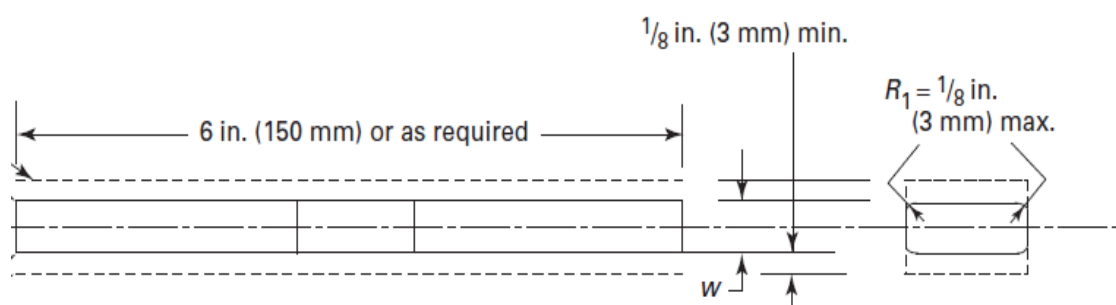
Croqui para usinagem corpo de prova de dobramento (ASME IX)
